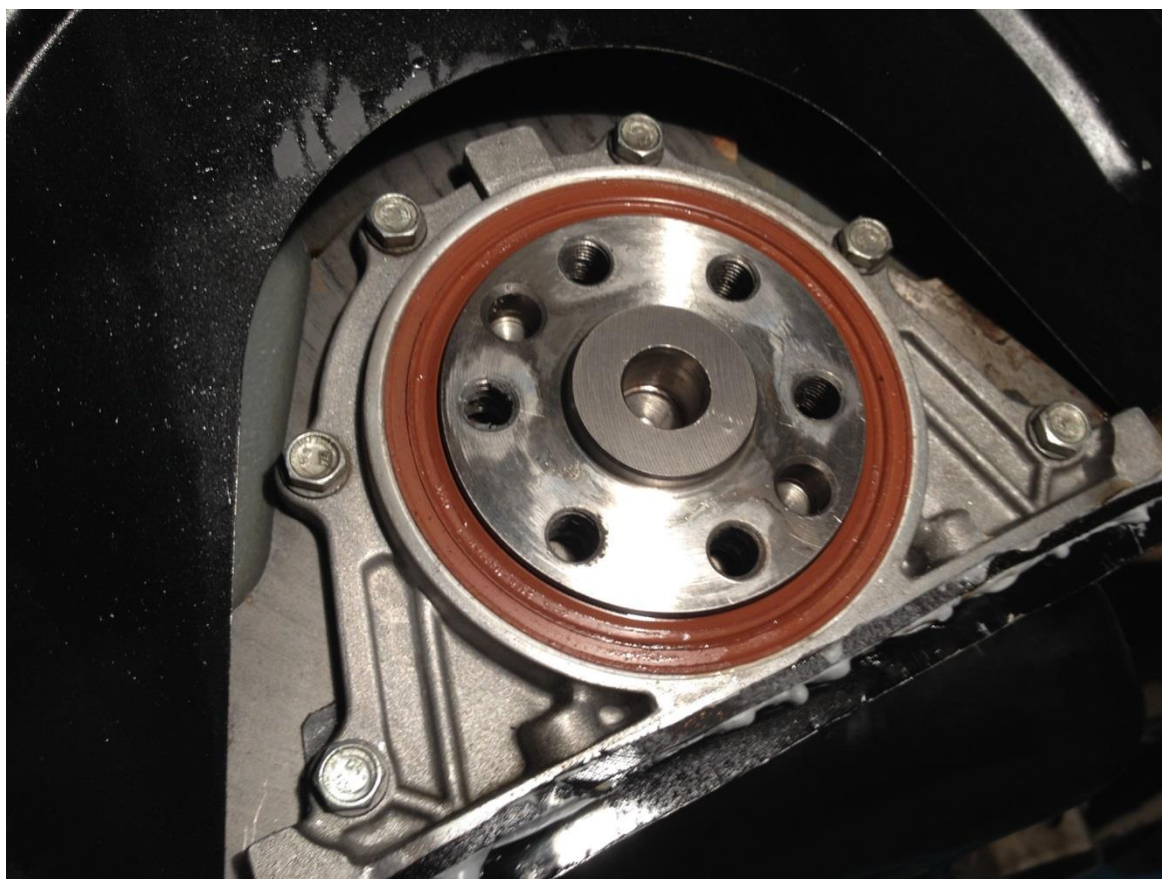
Вид детали - «Держатель заднего сальника коленчатого вала» в двигателе
